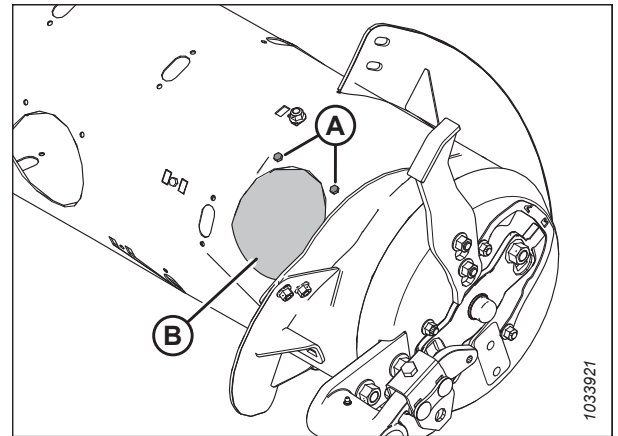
Tampa de acesso do sem fim - Lado direito
